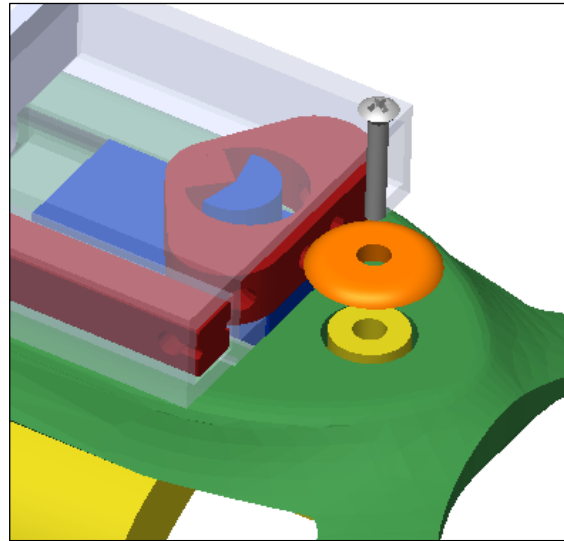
Nueva unión entre las piezas Rotating Gauntlet y Fixed Gauntlet explosionada
